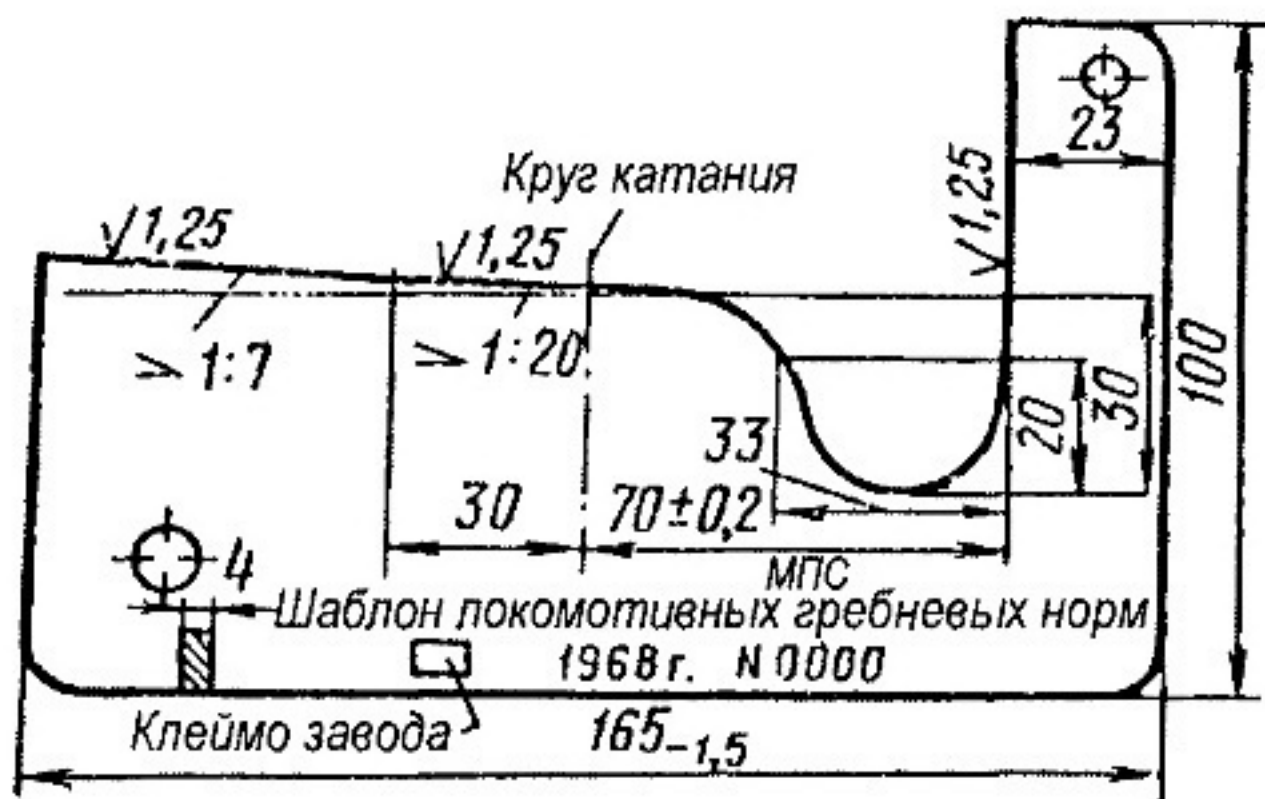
Типовой шаблон для проверки профиля бандажа после обточки поверхности катания колес
